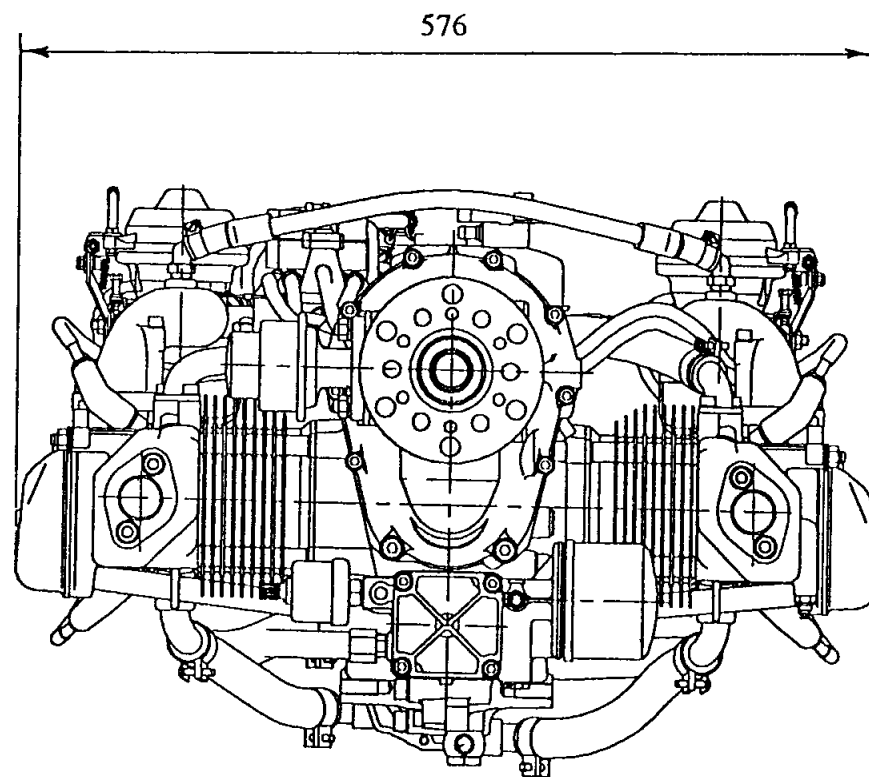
Двигатель «Rotax-912ULS». Чертеж общего вида
